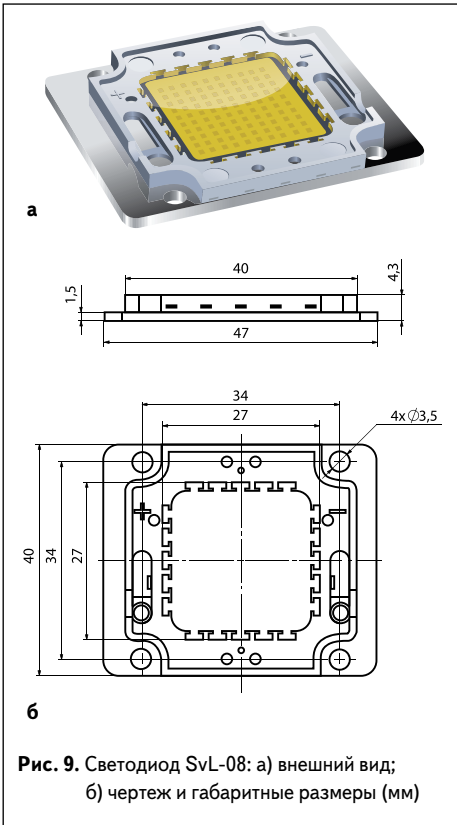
Светодиод SvL-08: а) внешний вид; б) чертеж и габаритные размеры (мм)
